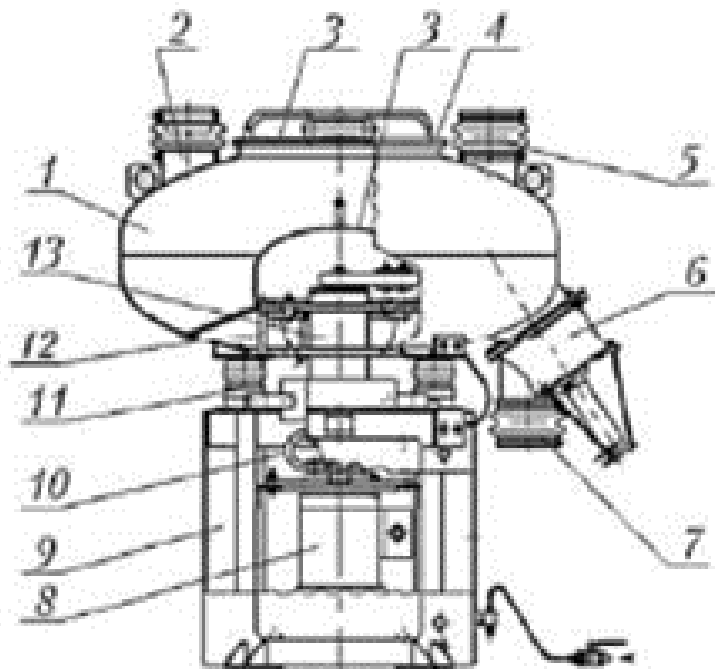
Устройство смесителя СмВ: 1 – камера; 2 – штуцер загрузки; 3 – крышки; 4 – хомут; 5 – уплотнитель; 6 – клапан; 7 – штуцер разгрузки; 8 – двигатель; 9 – рама; 10 – муфта; 11 – виброизолятор; 12 – болт; 13 – вибровозбудитель
